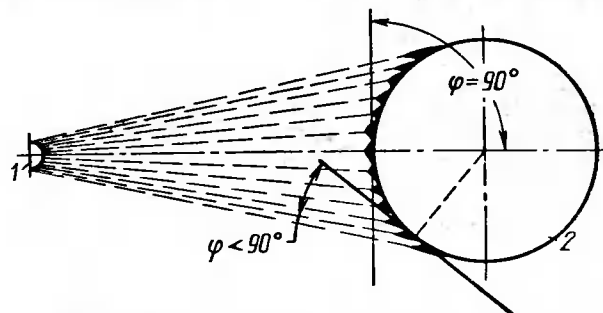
Схема падения металлических частиц на поверхность у цилиндрических деталей:
